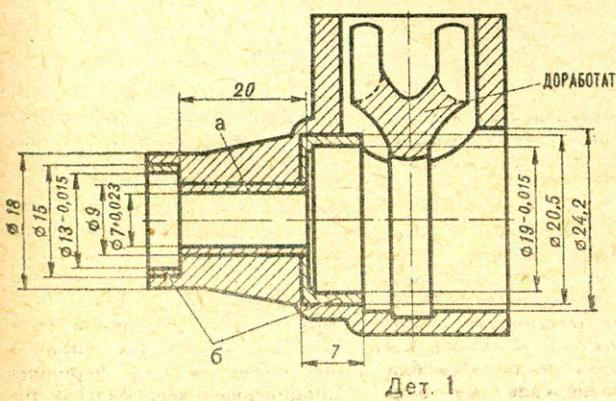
КАРТЕР ДВИГАТЕЛЯ.
